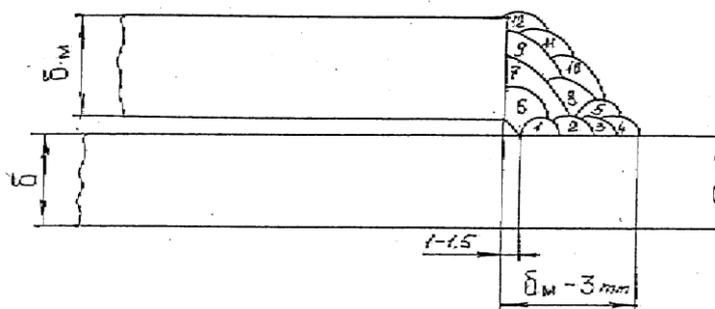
Последовательность наложения слоёв при сварке кольцевого углового шва муфты
